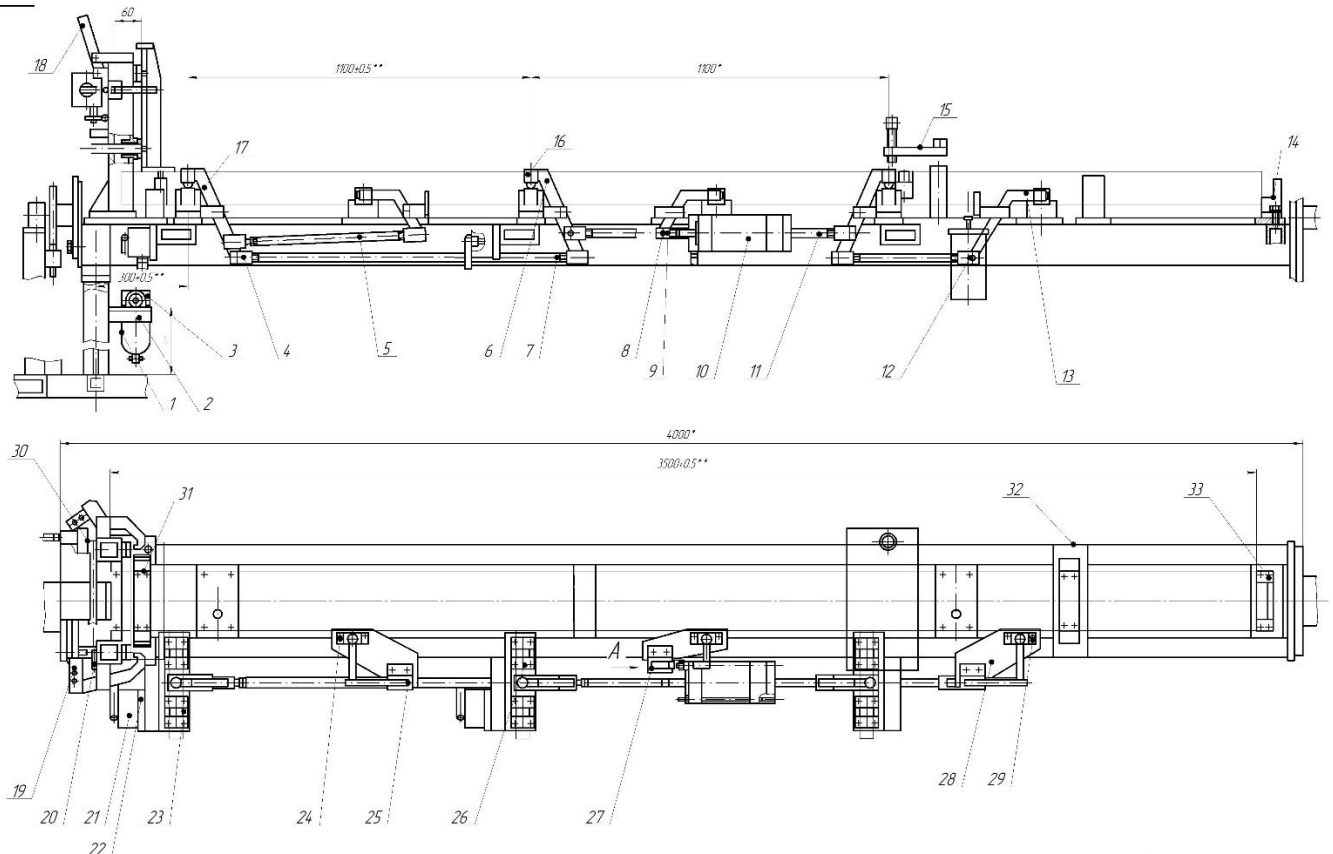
Кондуктор для складання та зварювання передньої балки
